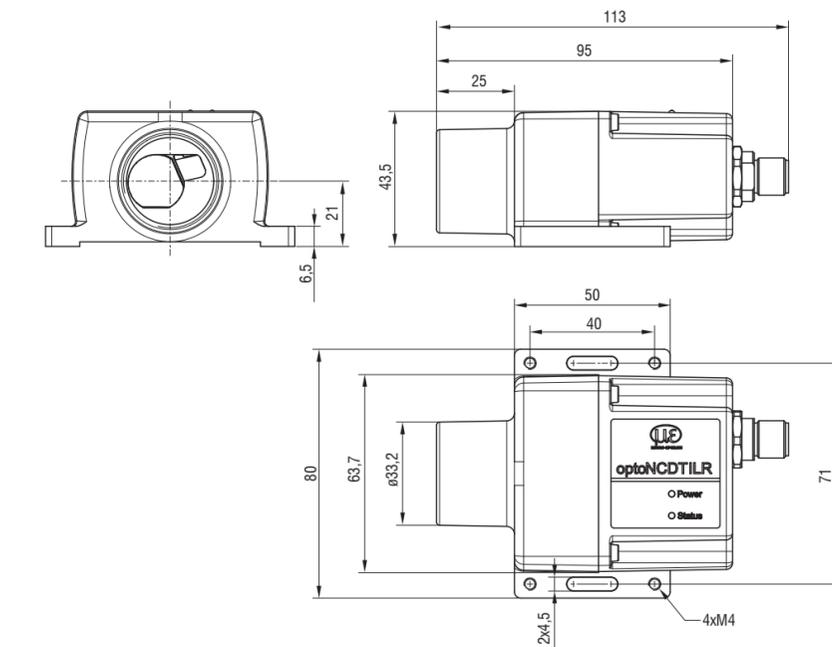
Maßzeichnung optoNCDT ILR3800-100, Abmessungen in mm
